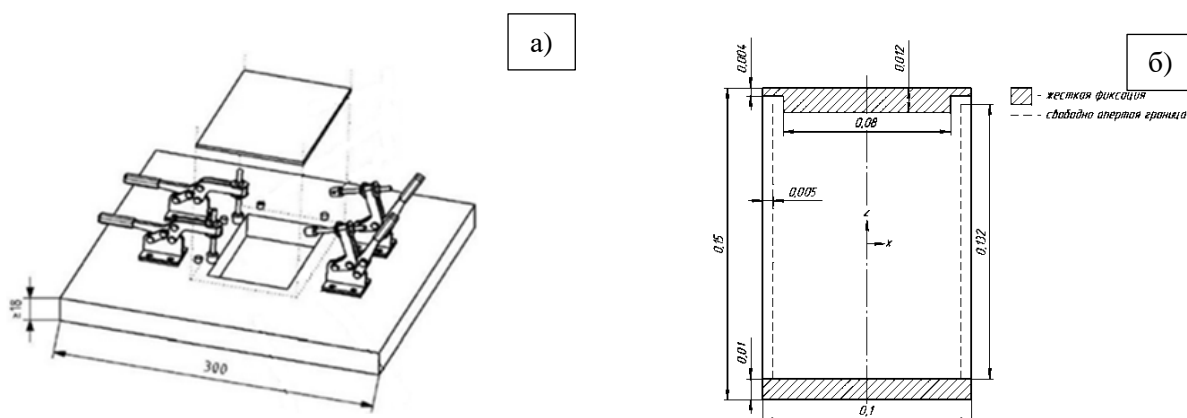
Схема закрепления образца для испытаний по стандарту:
